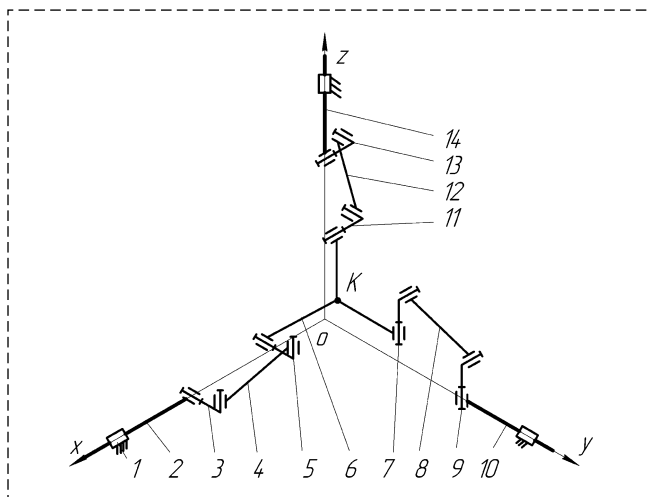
Самоустанавливающийся механизм с карданными шарнирами
